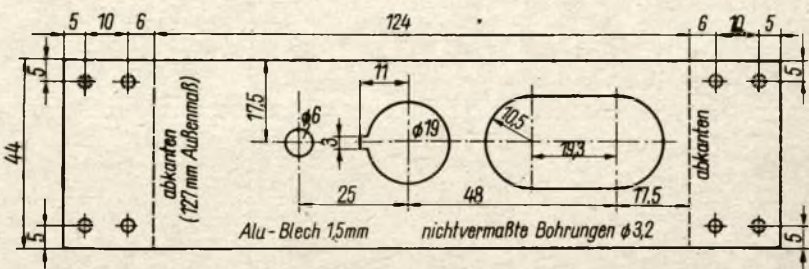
Maßskizze für Teil 6 (hinterer Chassiswinkel)
